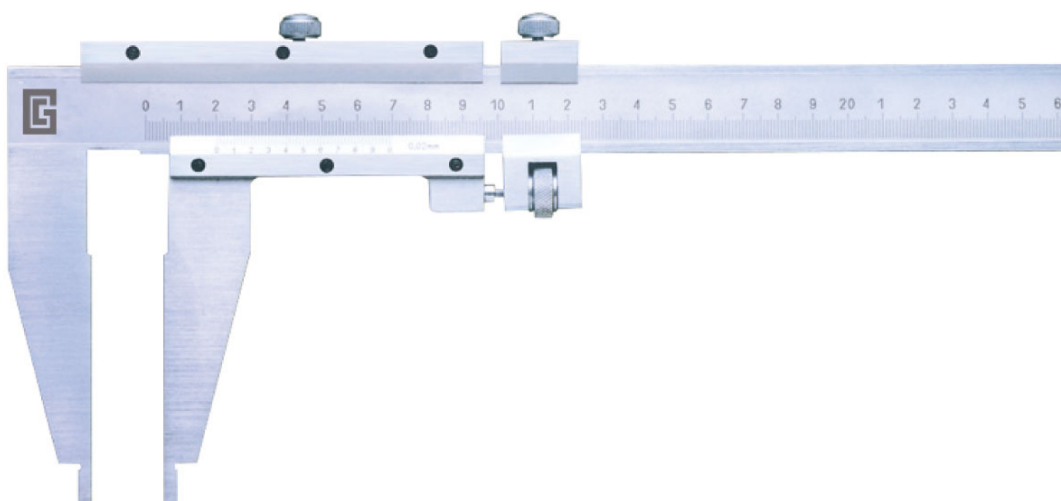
Общий вид штангенциркулей типа ШЦ-III.
